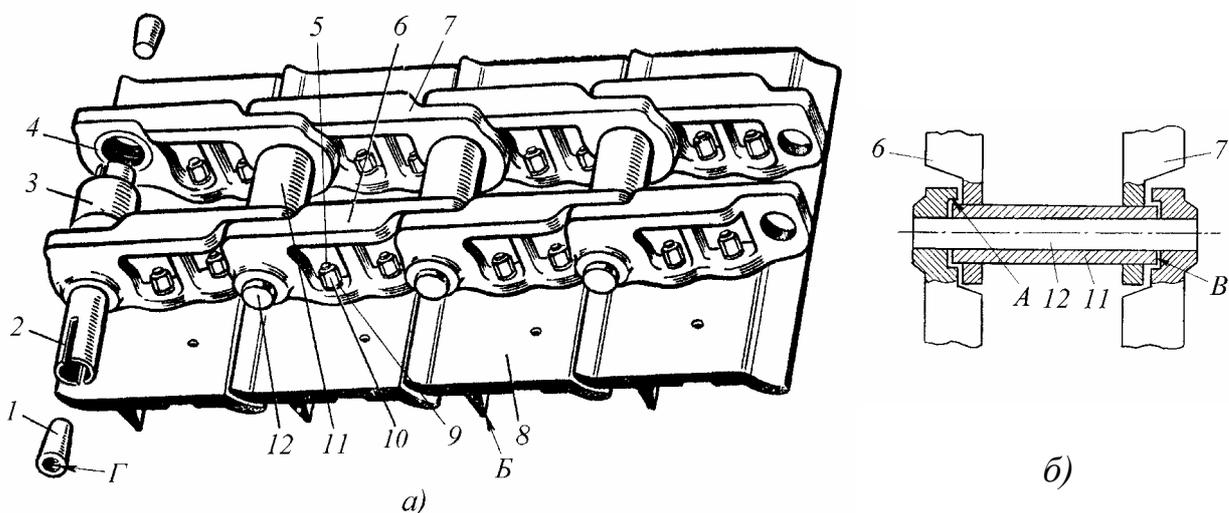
Составная гусеница рельсового типа с приподнятыми закрытыми шарнирами
